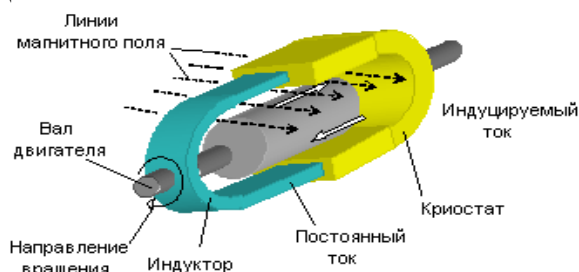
Сверхпроводниковое устройство для нагрева вращающейся цилиндрической алюминиевой заготовки в постоянном магнитном поле.
